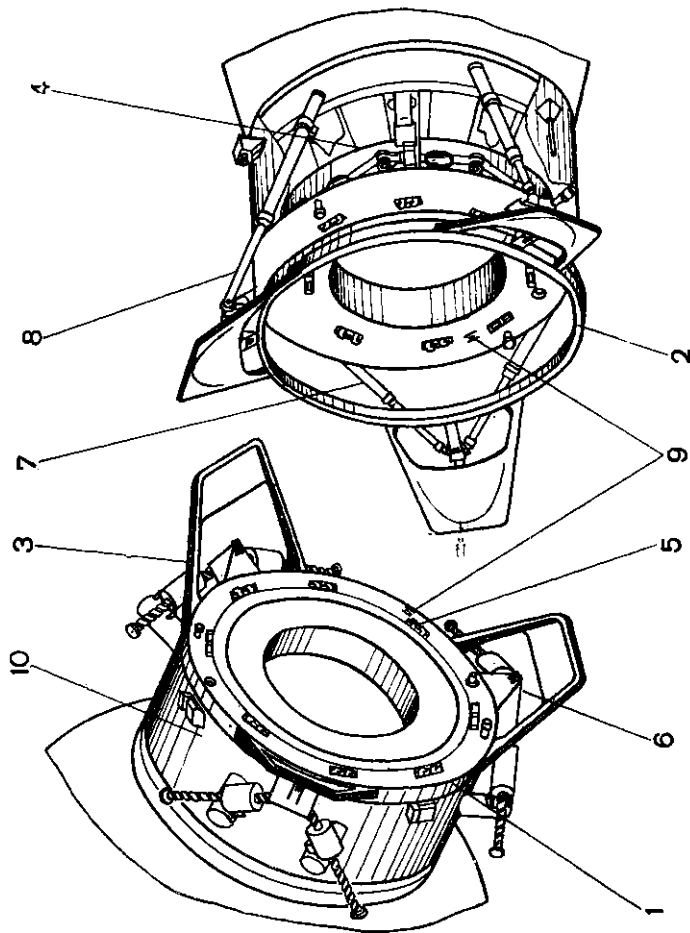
Упрощенный чертеж стыковочного устройства, показанного на рис. 1. Стыковка кораблей завершена, откинуты обе крышки и образован люк-лаз:
